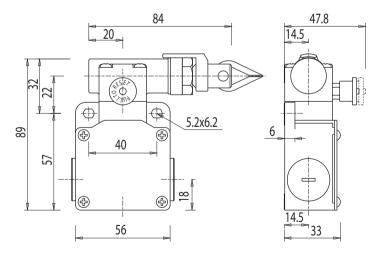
Dimensions de l'ERS200-MxC3x-HAR en mm
